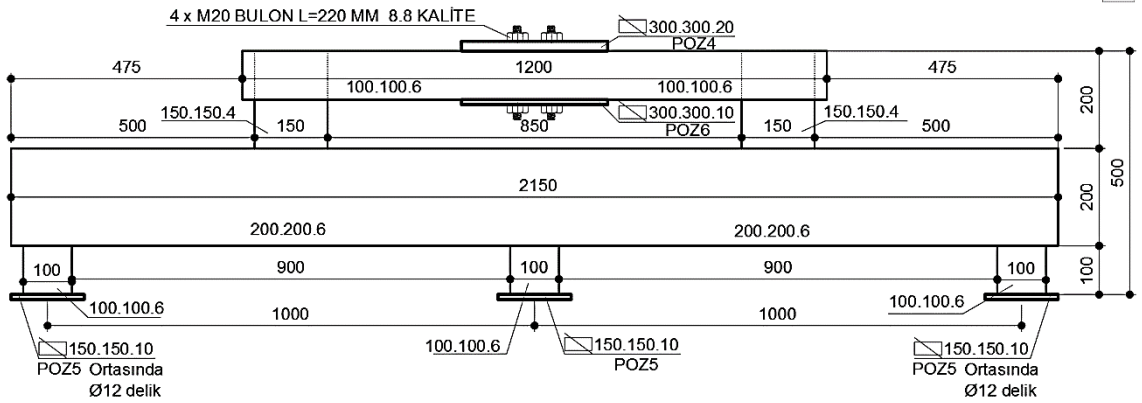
Aksel Yükleme Çelik Düzenğinin Konstrüksiyon Planı [51, 58]
